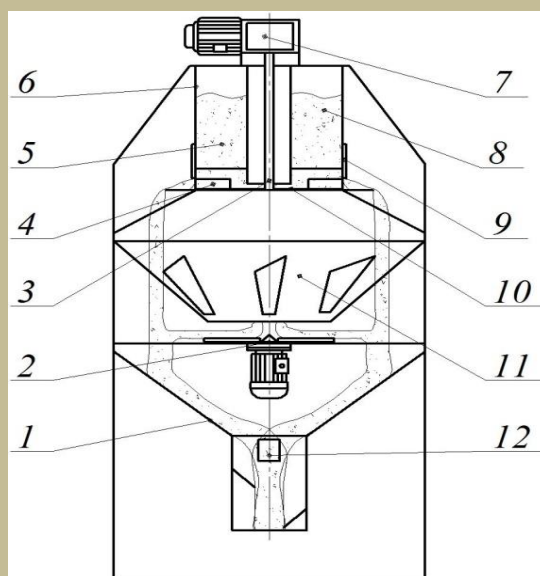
Схема дозатора-смесителя сыпучих кормов:
